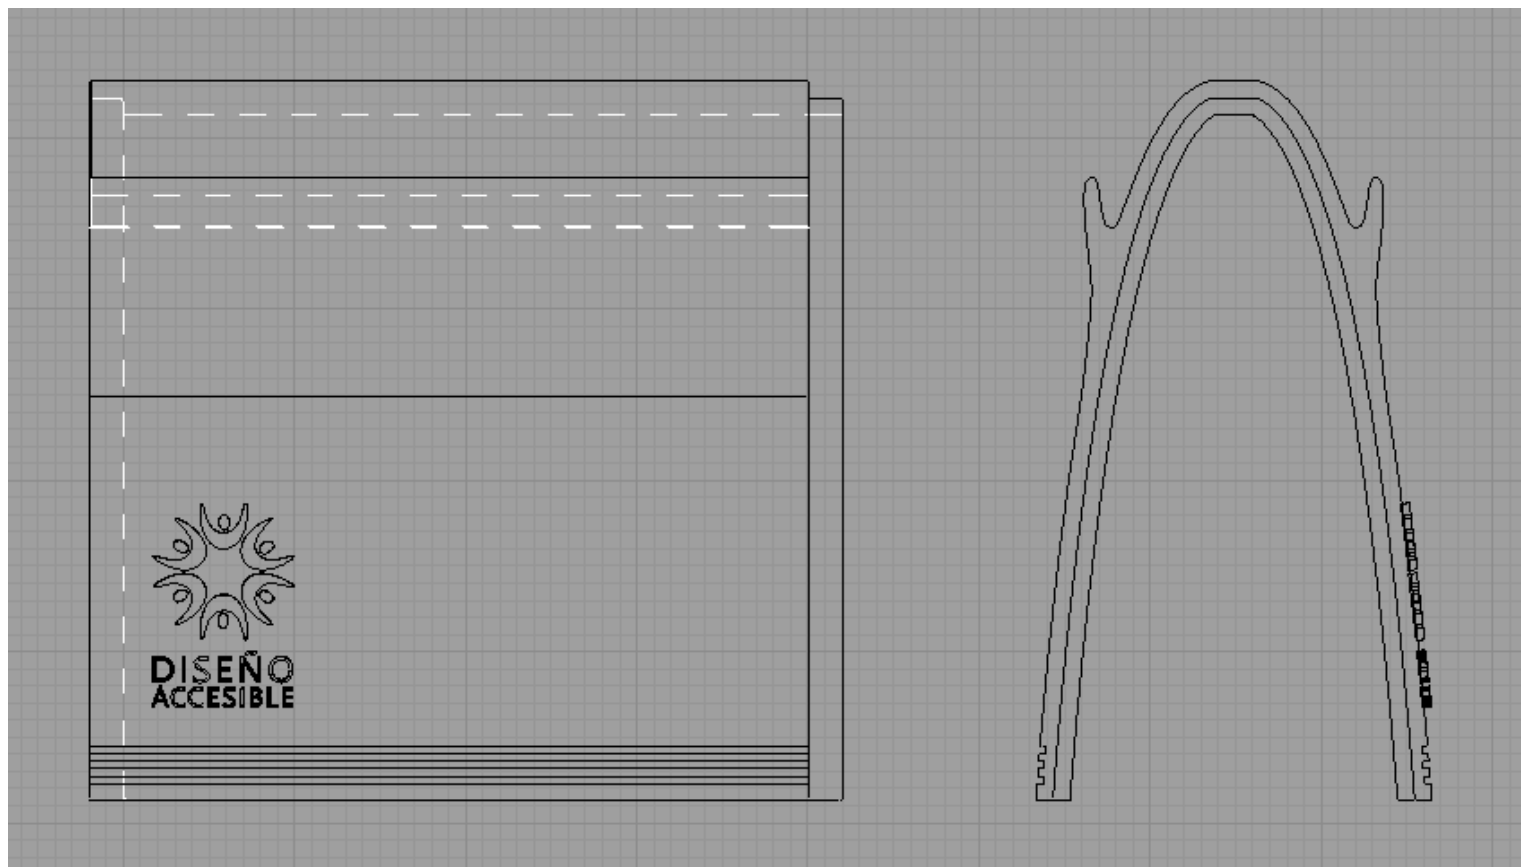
Planimetría Barrera Diseño Accesible. Elaboración propia.
